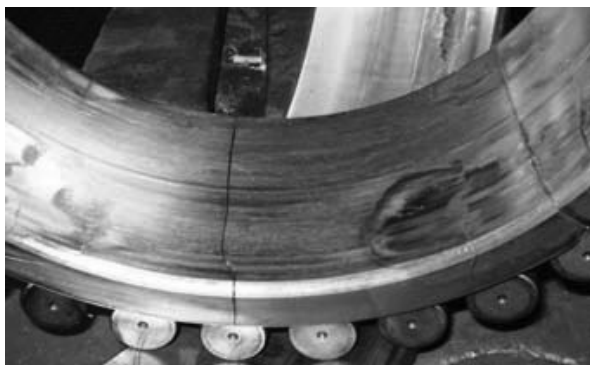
Трещина внутреннего кольца роликового подшипника
